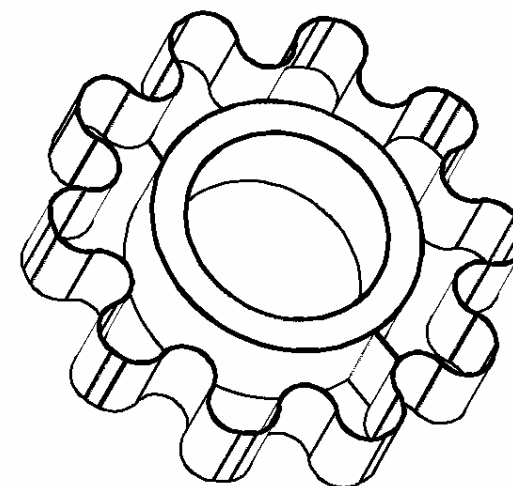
Изображение зубчатого колеса в AutoCad
